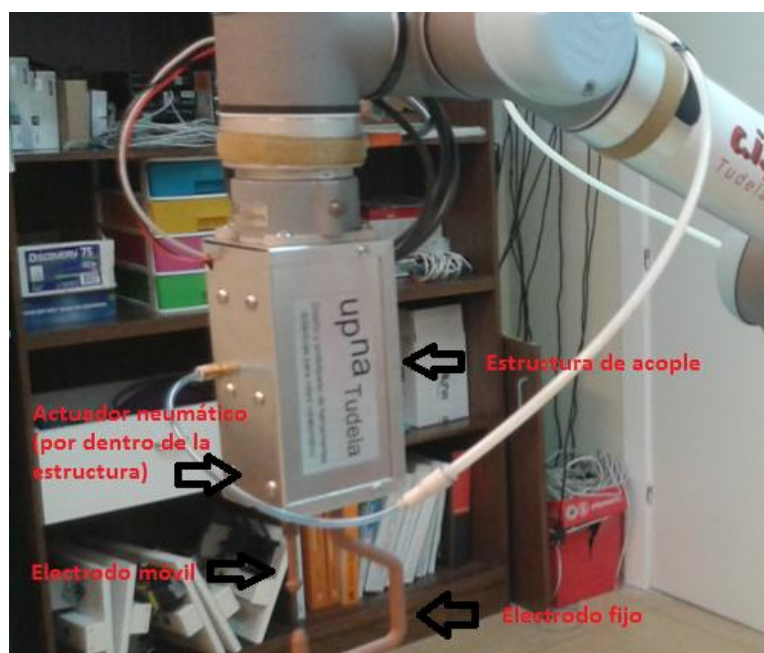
Pinza de soldadura tipo "C" instalada en el robot UR5
